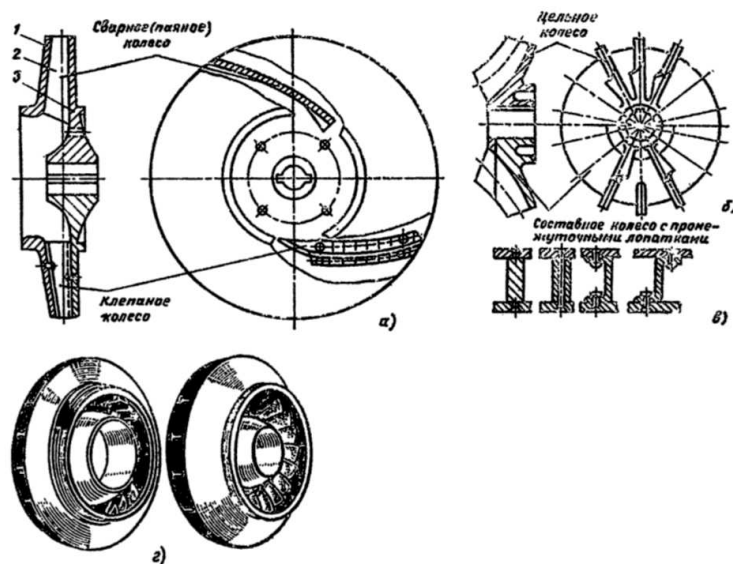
Рабочее колесо центробежных компрессоров: а - закрытого типа; б - полуоткрытого типа; в - способы клепки лопастей; г - общий вид закрытого колеса с пространственными лопастями
